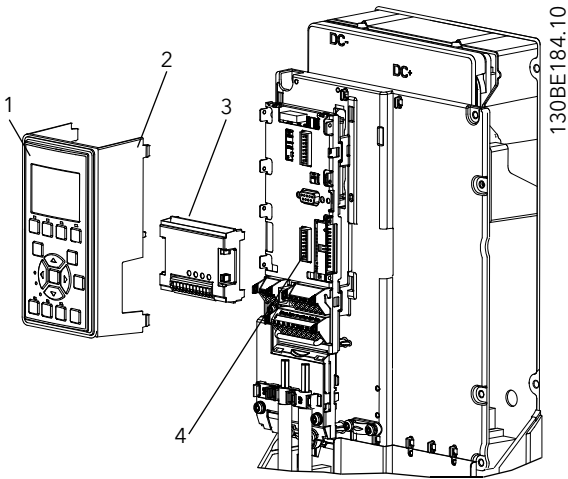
Установка корпусов размера A5, B1, B2, C, D
